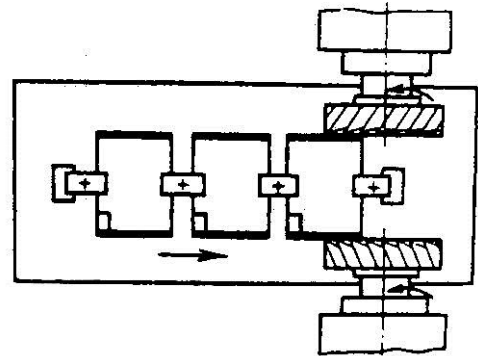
Комбіноване фрезерування на поздовжньо-фрезерному верстаті
